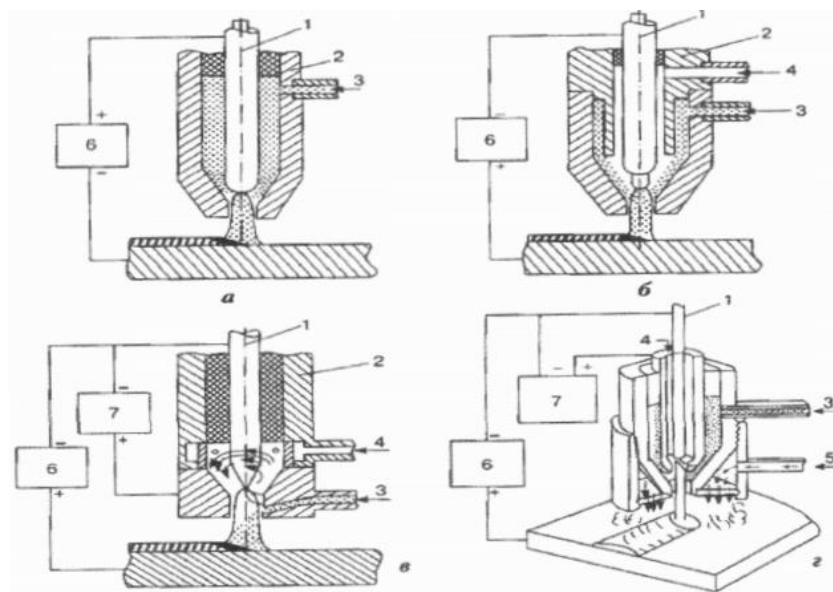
Схеми плазмового наплавлення з введенням присадочного порошку в дугу всередині плазмотрона: а - разом з плазмоутворюючим газом; б - через електродну камеру; в - через бічний отвір в каналі сопла; г - через воронкоподібну щілину між соплами (1 - мідний водоохолоджуваний електрод (а), водо охолоджуваний з вольфрамовою вставкою (б), вольфрамовий (в, г), 2 - сопло; 3 - введення присадочного порошку з транспортуєчим газом; 4 - введення хіазмо утворюючого газу; 5 - введення захисного газу; 6 - джерело живлення дуги прямої дії; 7 - джерело живлення непрямої дуги).
